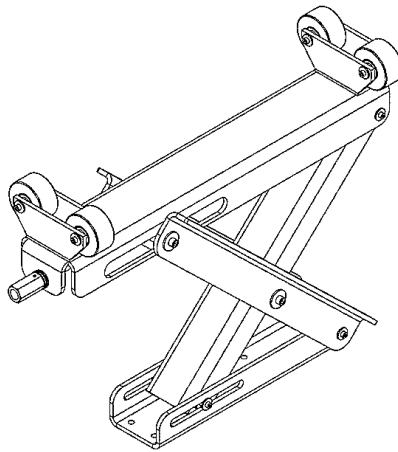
Perspetiva isométrica " Assembly final preguiça".
